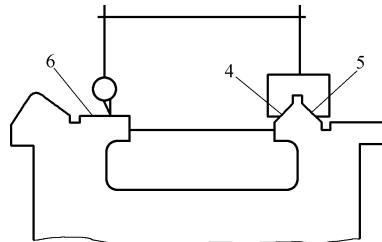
V形导轨平面4、5与平面导轨平面6的平行度测量
